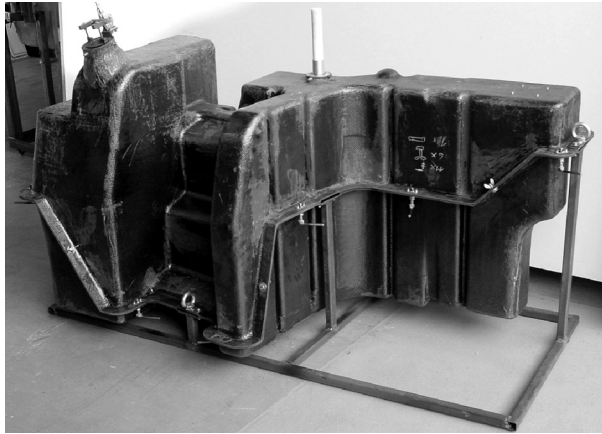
Prototypenwerkzeug mit Kohlefaserformschalen
